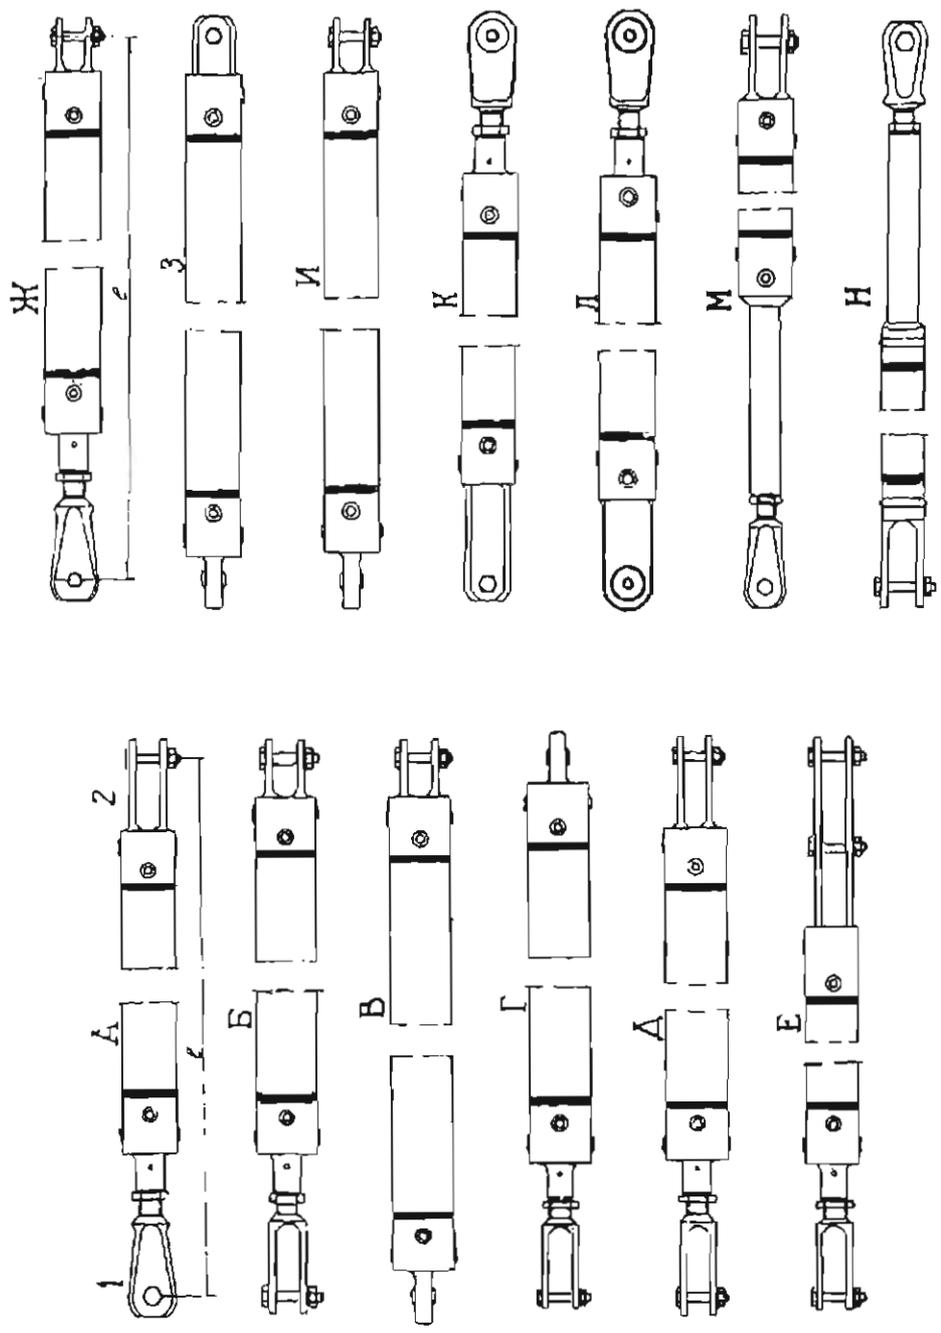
Kennzeichnung der Steuerstangen der Querruder
